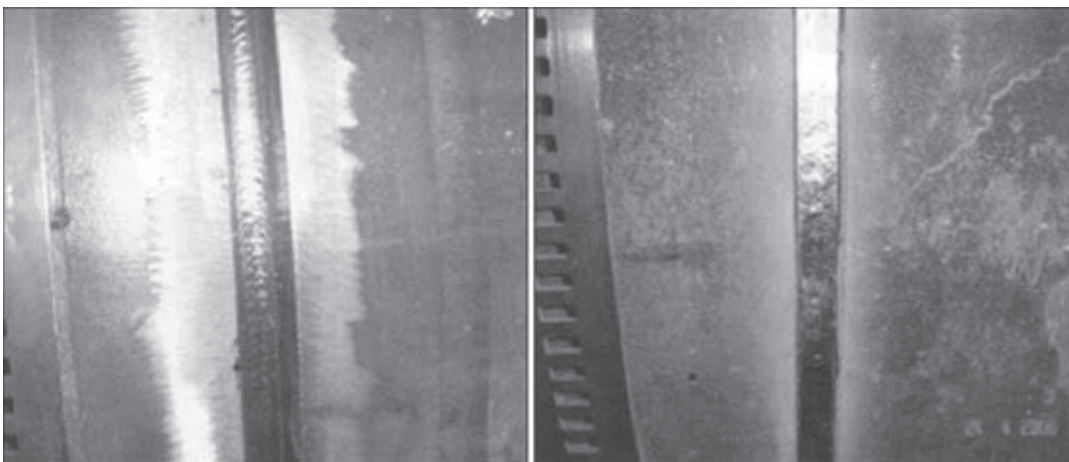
Внешний вид сварного соединения, выполненного процессом MIG/MAG
